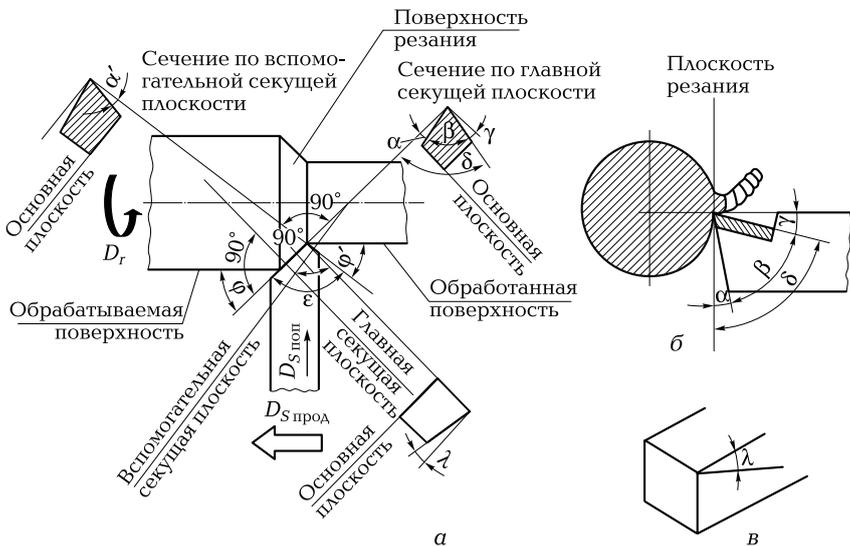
Основные поверхности заготовки, движения, осуществляющие процесс резания, углы резца:
